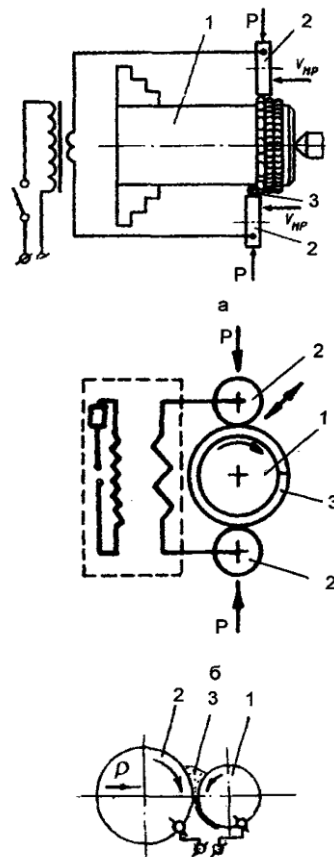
Схеми контактеного наварювання дроту (а), стрічки (б) та порошку (в) на деталі типу “вал”: 1 – наварювана деталь; 2 – ролик-елетрод; 3 – присадний матеріал.
